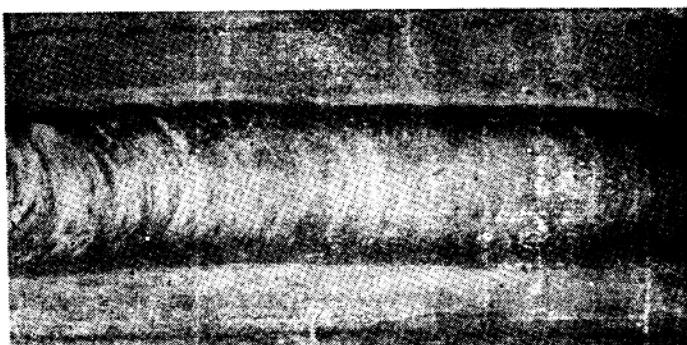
4 硬规范焊接的焊缝外形 (LD10, J16)
